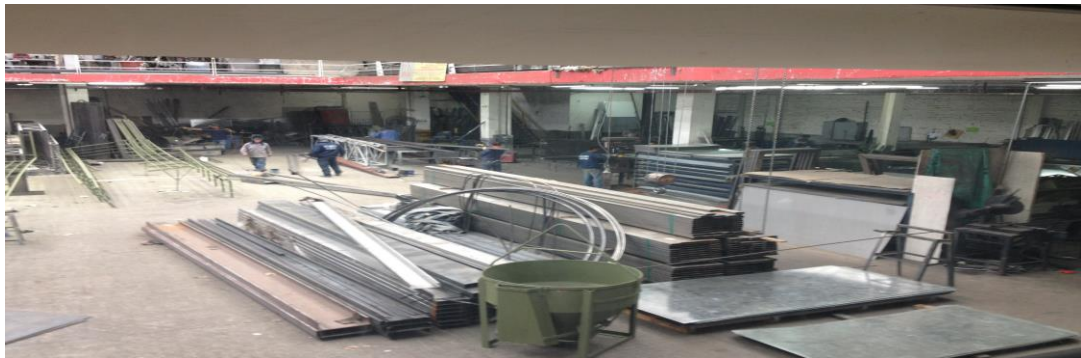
Fotografía Acero Carbón- primera planta de la empresa
